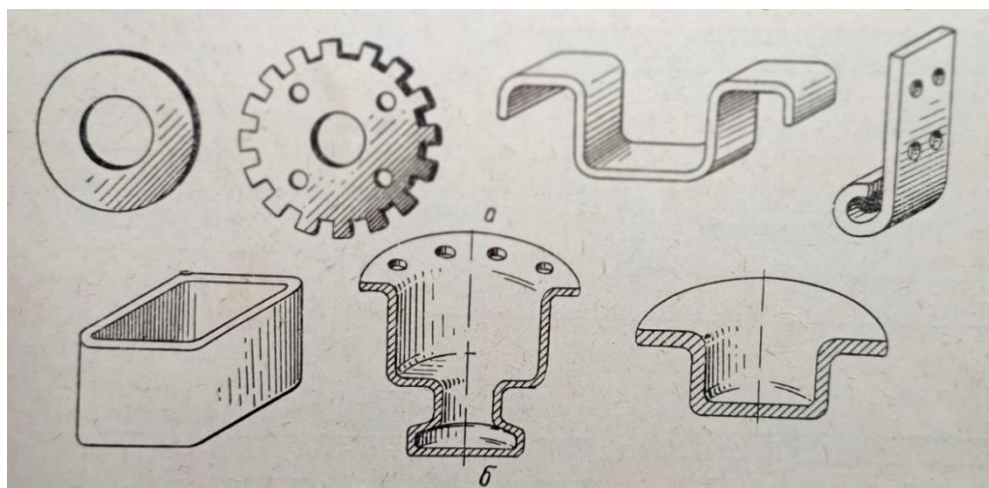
Деталі, виготовлені листовим штампуванням
